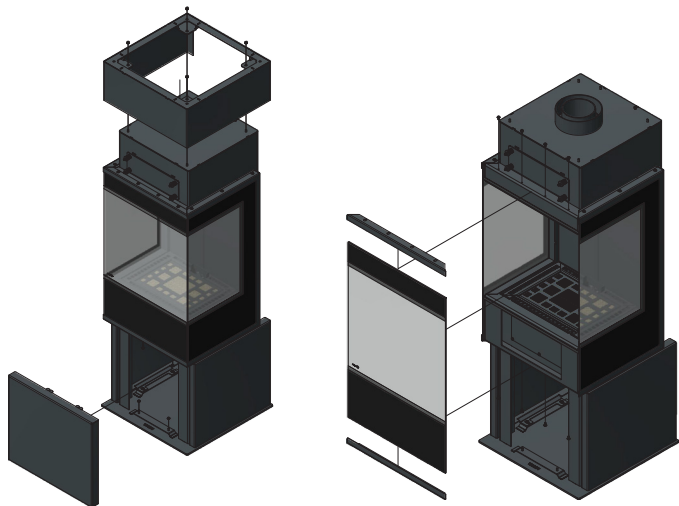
THOR VIEW GAZ - demontaż górnej pokrywy i tylnej ściany
